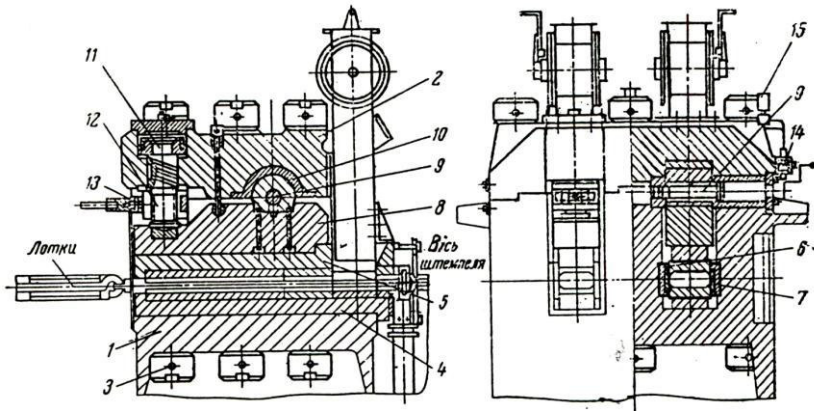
Головка торфобрикетного преса [1, с.222]
